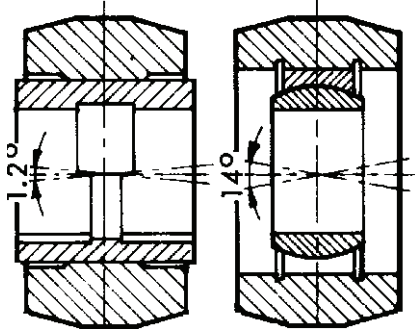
Проушина и втулка для крепления с шаровым шарниром
